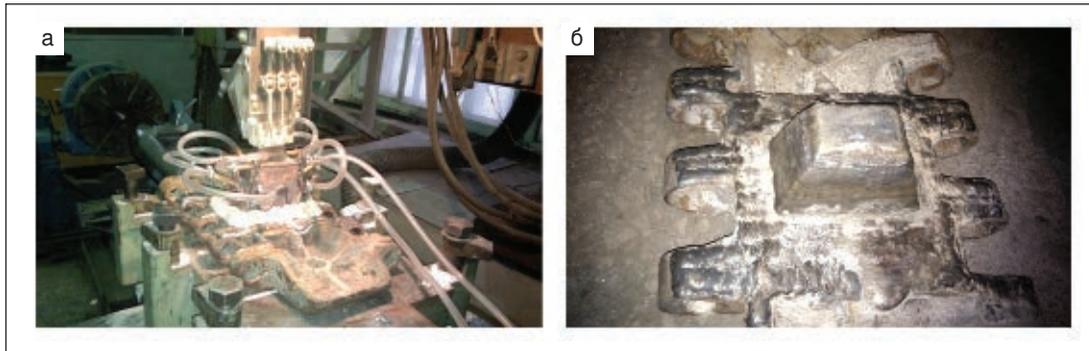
Электрошлаковая наплавка шипа трака двумя лентами: а — процесс наплавки; б — восстановленный шип трака крана РДК-25
